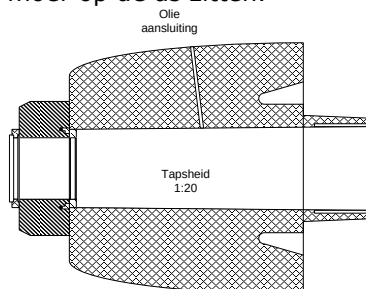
Hydraulische bevestiging schroef. Bron: Wärtsilä.
